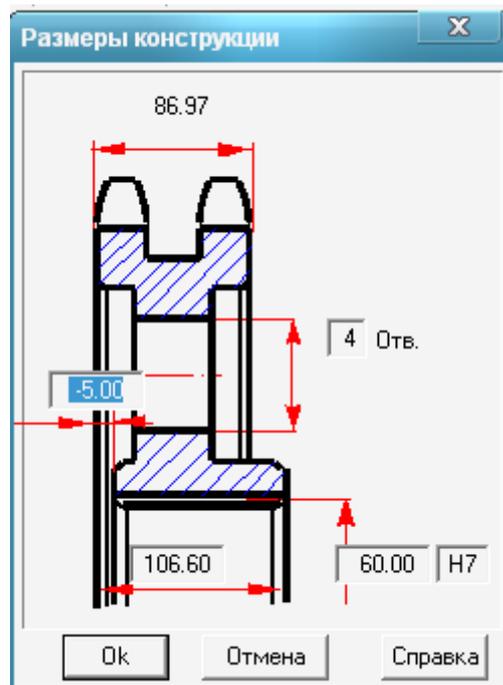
Определение размеров ступицы и количества отверстий в диске звёздочки, - «Размеры конструкции».
